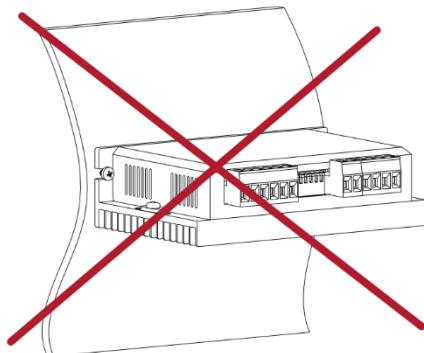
неверный монтаж драйвера: ребра расположены горизонтально под корпусом
